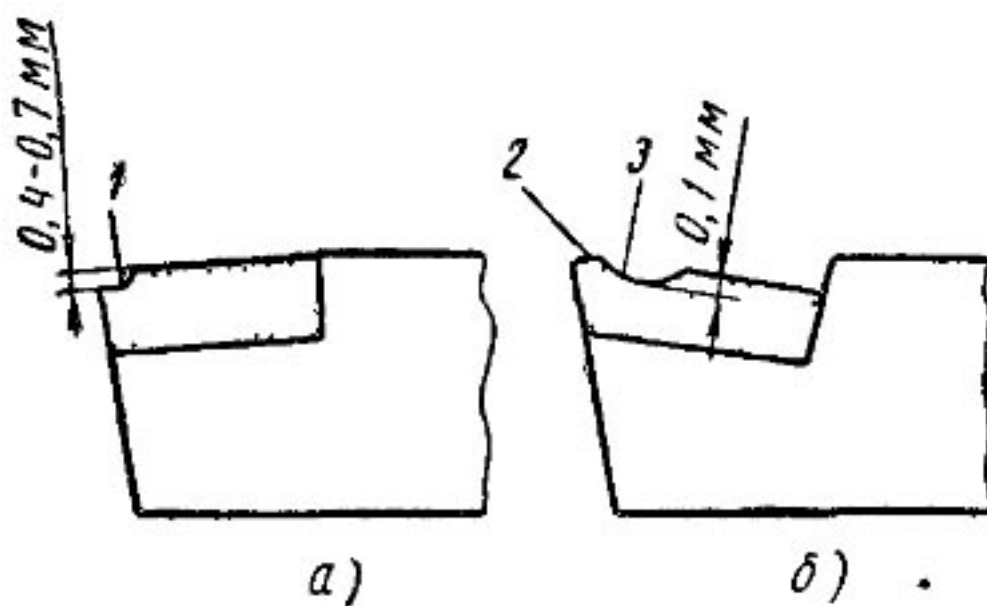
Передняя поверхность резца с пластиной из твердого сплава
